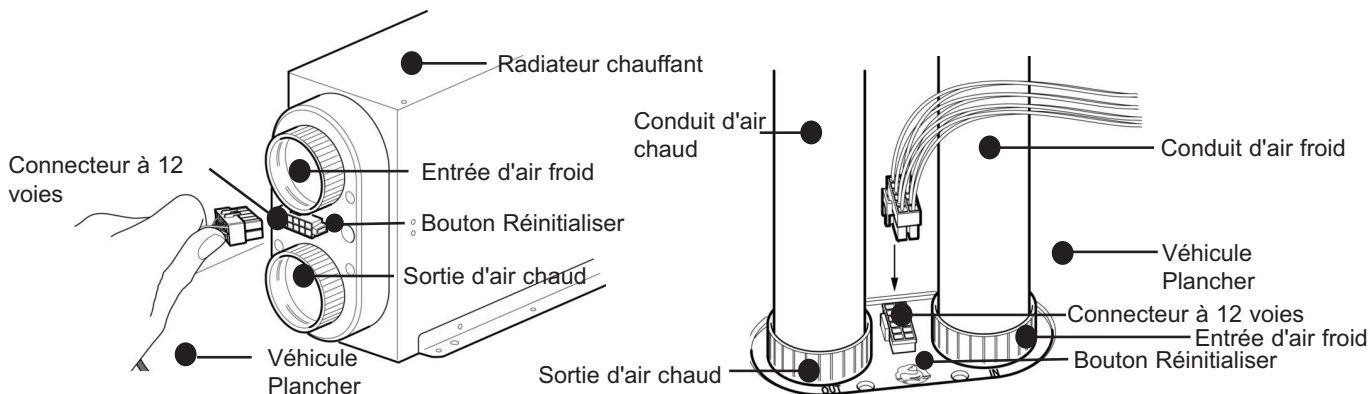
Installation interne - Raccordement au 12 V d.c. Fig. 32 Installation sous plancher - Raccordement au 12 V d.c.
